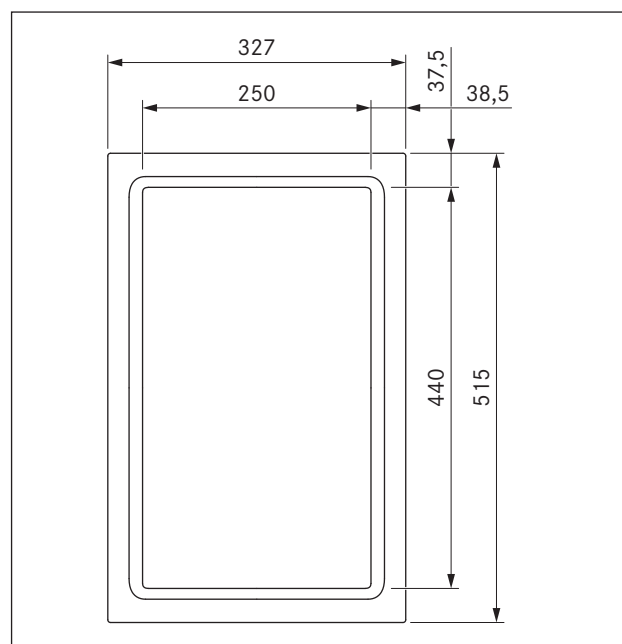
Dimensões do aparelho CKT, vista de cima
